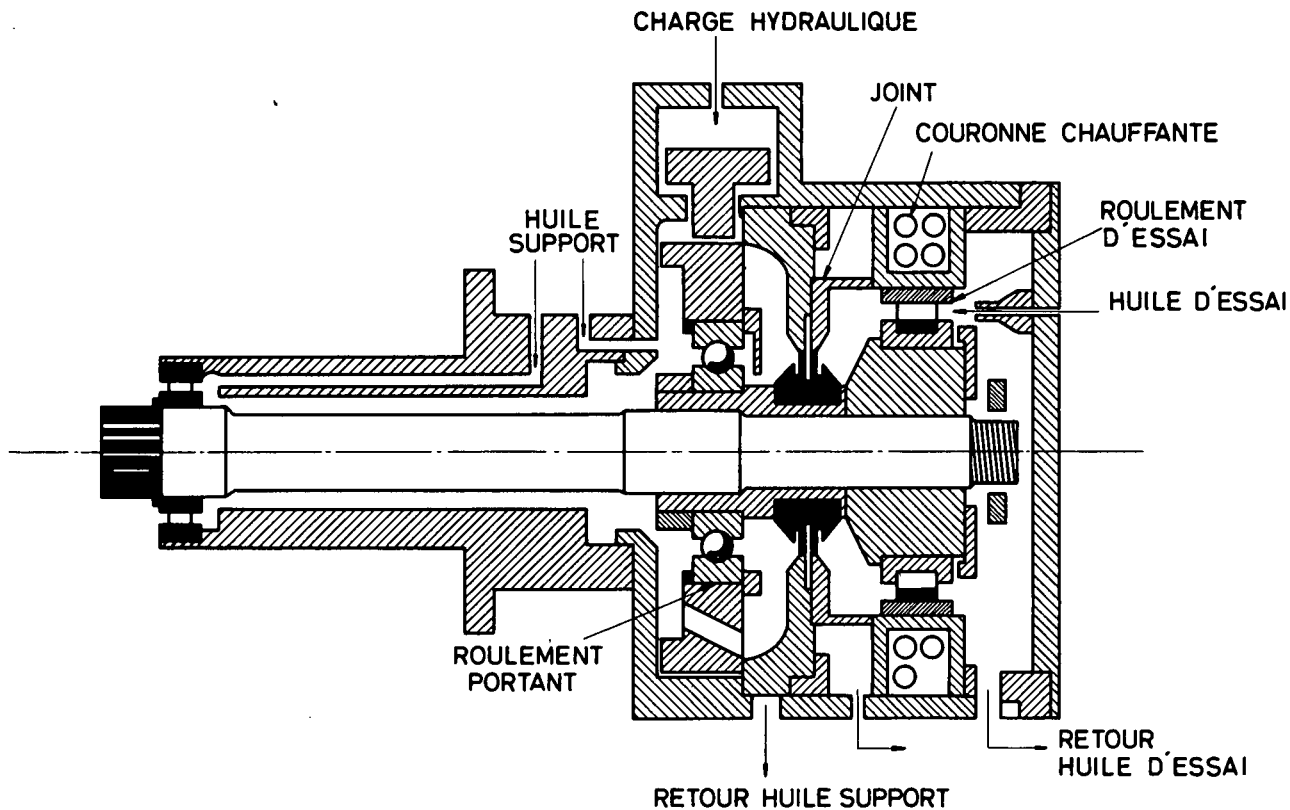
Essai ERDCO. Schéma de la tête d'essai
